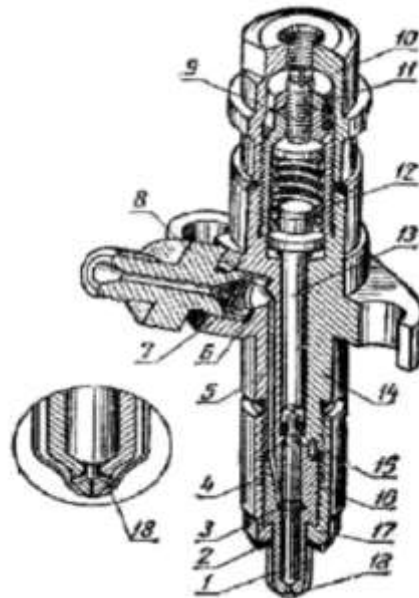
Форсунка: 1 - голка розпилювача: 2 та 6 - прокладки: 3 - кільцева камера; 4 та 5 - канали підведення палива до розпилювача; 7 - фільтр: 8 - штуцер: 9 - регулювальний гвинт: 10 - ковпак: 11 - контргайка: 12 - пружина: 13 - штанга: 14 - корпус форсунки: 15 - штифт: 16 - корпус розпилювача;
